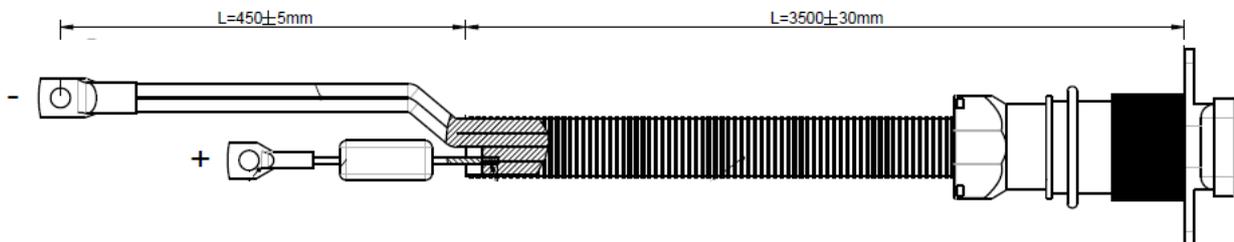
Cavo ISO 12369 per collegamento diretto alla batteria
